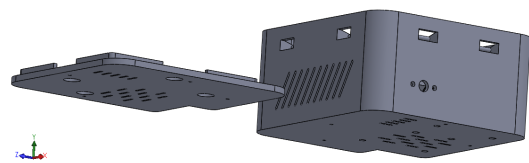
Posición final de impresión del cuerpo principal y del acoplamiento.
